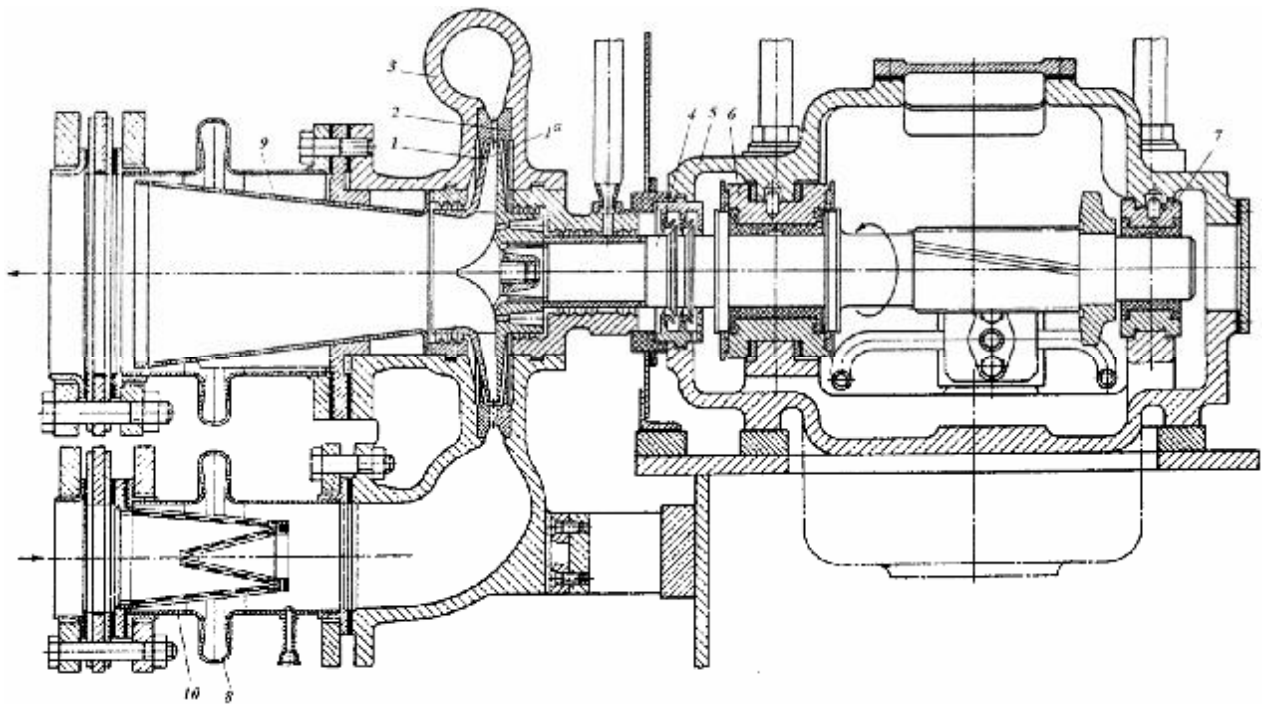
Продольный разрез радиального воздушного турбодетандера реактивного типа: 1 – рабочее колесо; 1, а – лопатки; 2 – направляющий аппарат; 3 – корпус турбодетандера со спиральным подводом воздуха; 4 – вал с быстроходной шестерней редуктора; 5 – корпус редуктора; 6 – опорно-упорный подшипник; 7 – опорный подшипник; 8 – компенсаторы температурных деформаций; 9 – выходной диффузор; 10 – сетчатый фильтр
